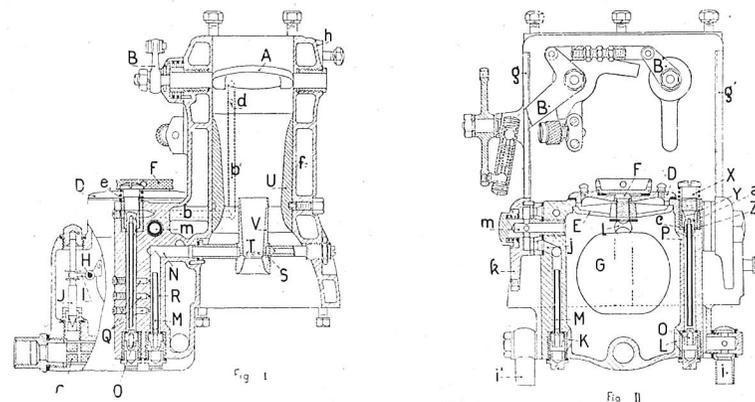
VUE DES CARBURATEURS « ZÉNITH » 60 J. et D. J.
